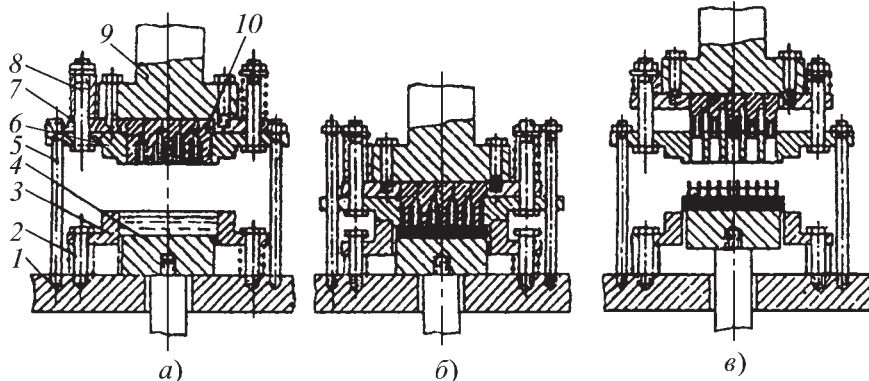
Пресс-форма для пуансонно-поршневого прессования нескольких алюминиевых заготовок массой 0,01 кг каждая:
